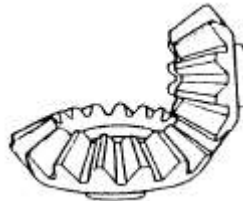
Roda Gigi Kerucut (*bevel gear*)
